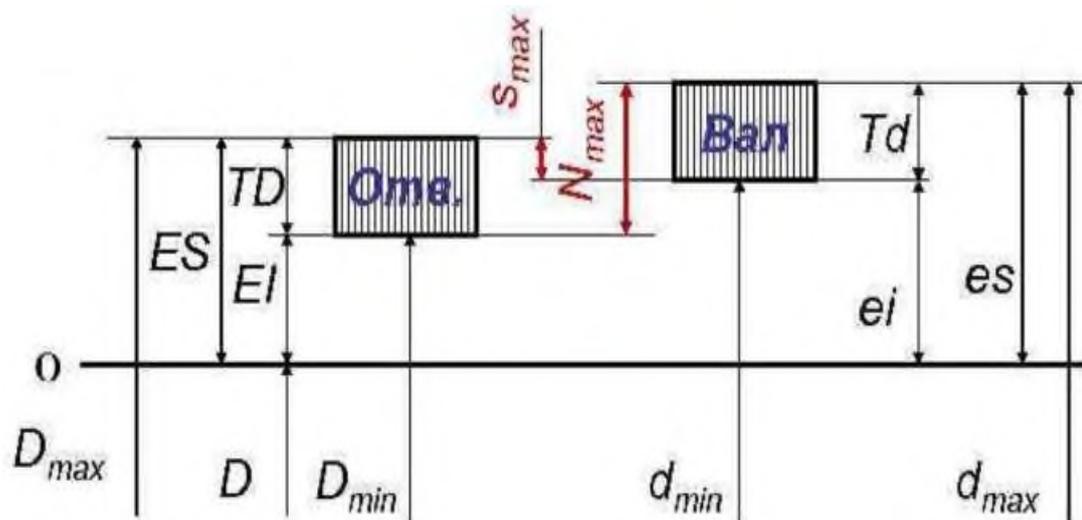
Поля допусков отверстия и вала при переходной посадке
